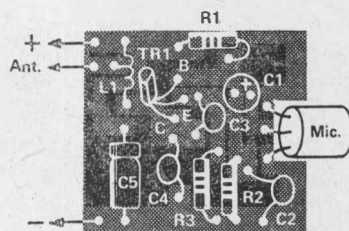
Disposição dos componentes sobre a plaqueta da Fig. 2.
